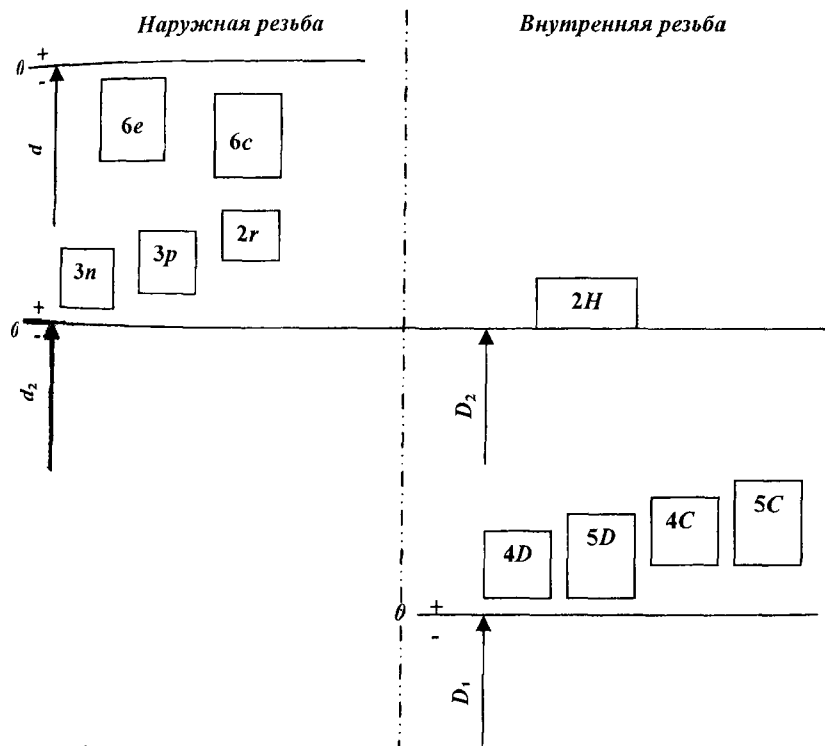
Поля допусков резьб для соединений с натягом
